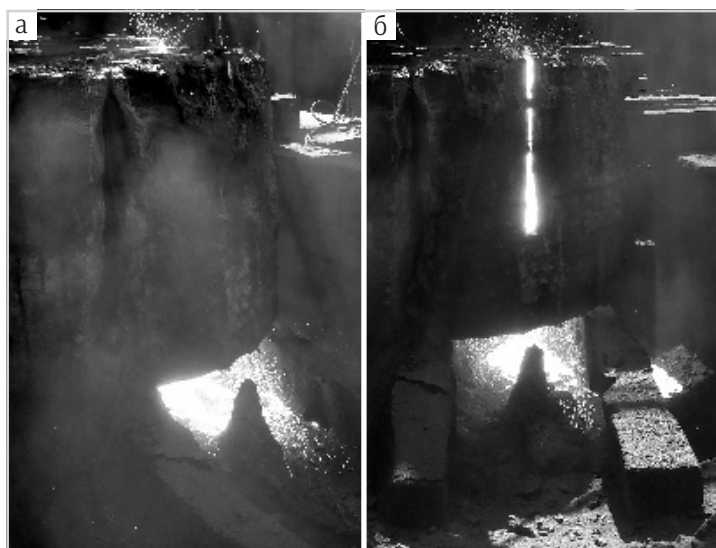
Кислородная резка поковки толщиной 1700 мм из стали 34ХМФ: а — вид сбоку; б — вид спереди
